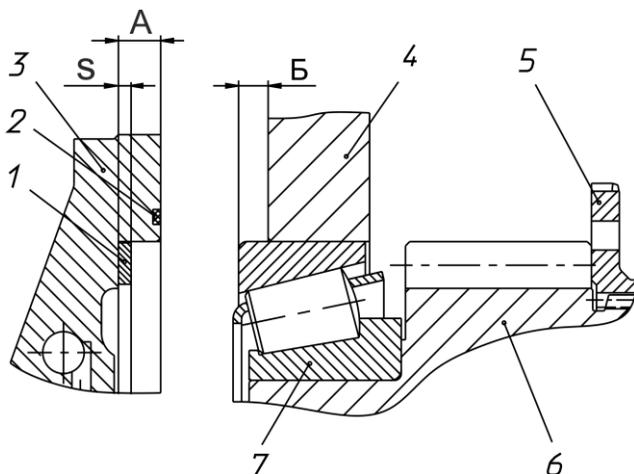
Регулировка конических подшипников первичного и вторичного валов:
